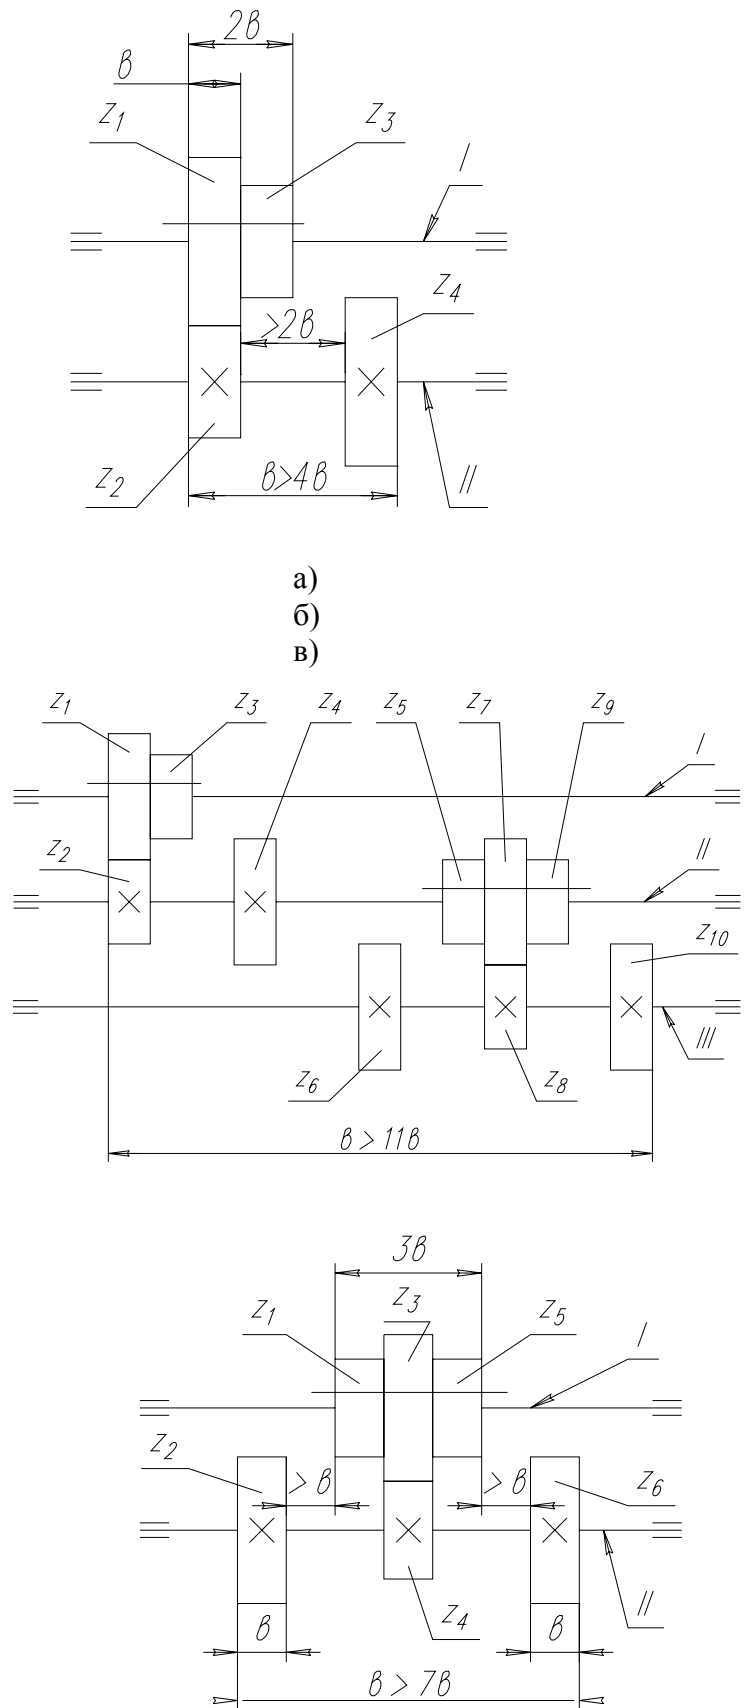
Механизмы с передвижными блоками зубчатых колёс
